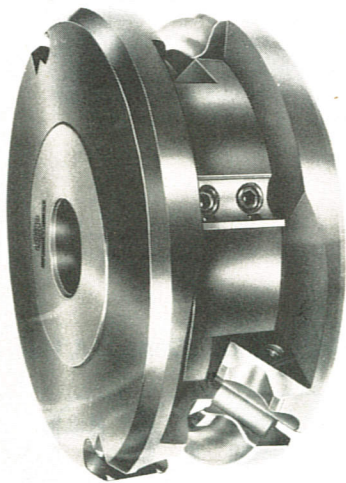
dreboform-Diamant-Profilfräser in BG-Test-Ausführung
